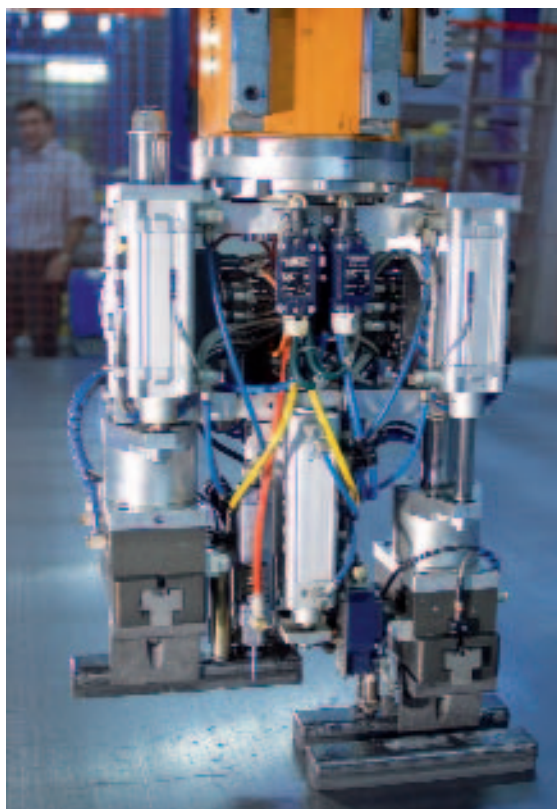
Компактный грейферный механизм для установки магнитных прижимов для пазов.
